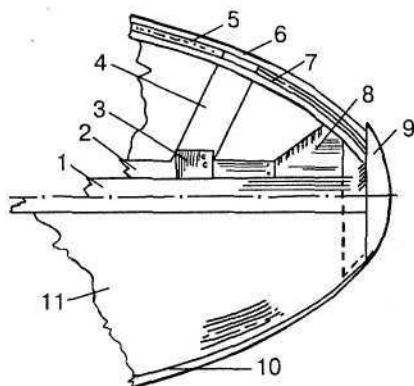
Детали носа байдарки-челнока: 1 — мидельвейс; 2 — киль; 3 — флор; 4 — шпангоут двойной; 5 — уплотнение; 6 — стрингер подпалубный; 7 — привальный брус внутренний; 8 — форштевень; 9 — водорез; 10 — буртик; 11 — палуба
